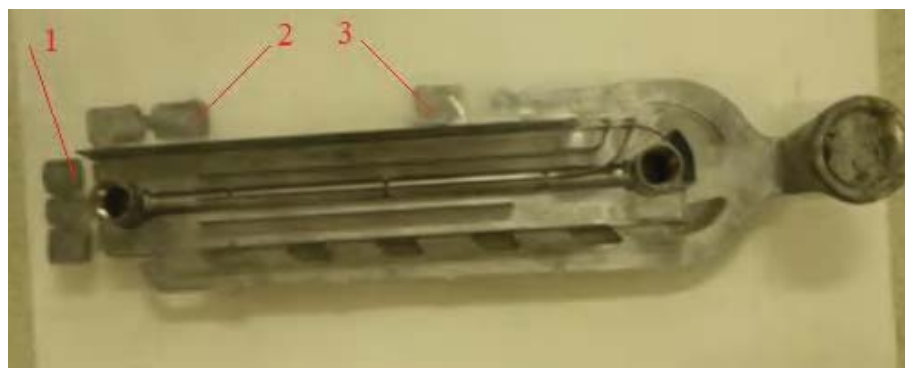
Образец № 3–2 – отливка с литниково-питающей системой:
